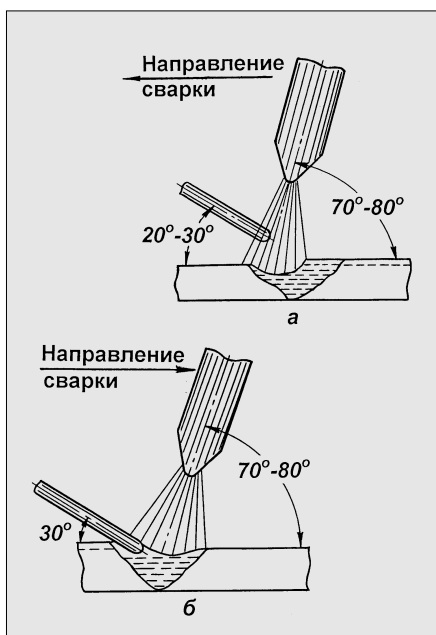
Схема «левого» (а) и «правого» (б) способов сварки с подачей присадочного материала
